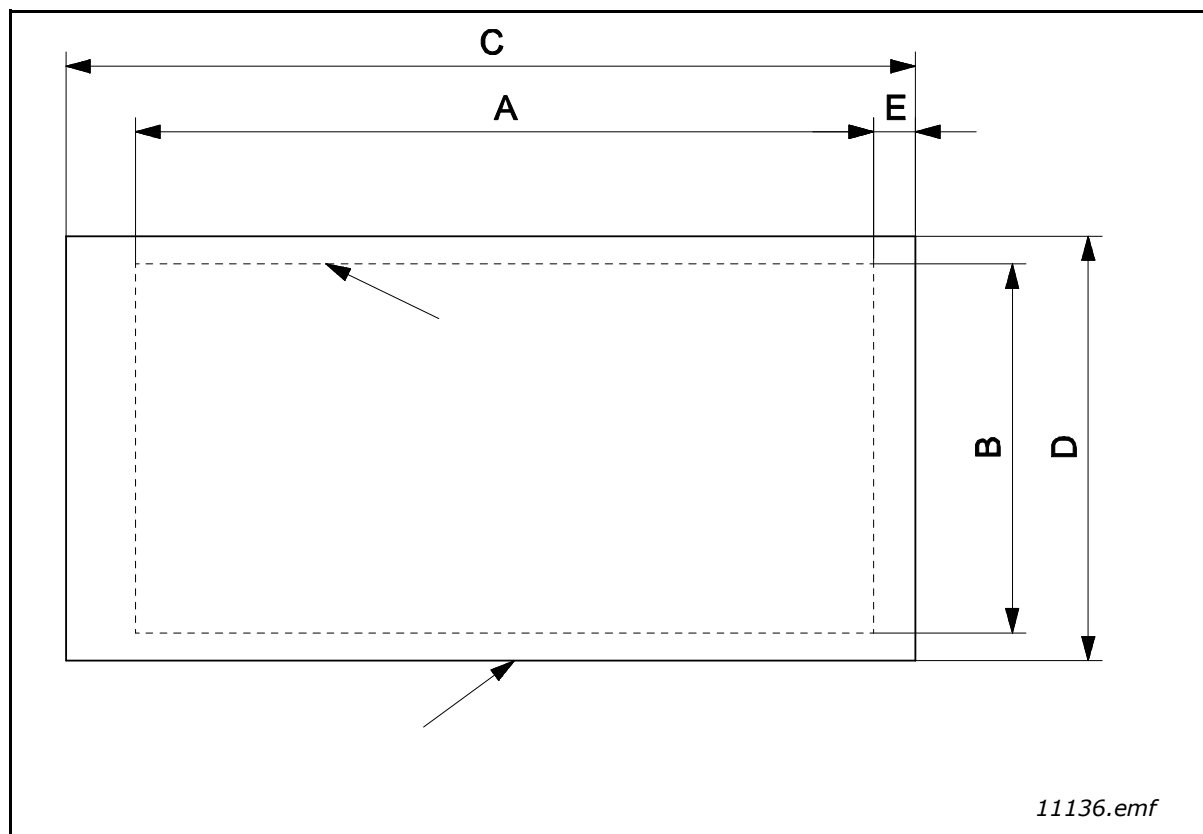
Dimensions de découpe en montage par brides, tailles MR4 à MR9
